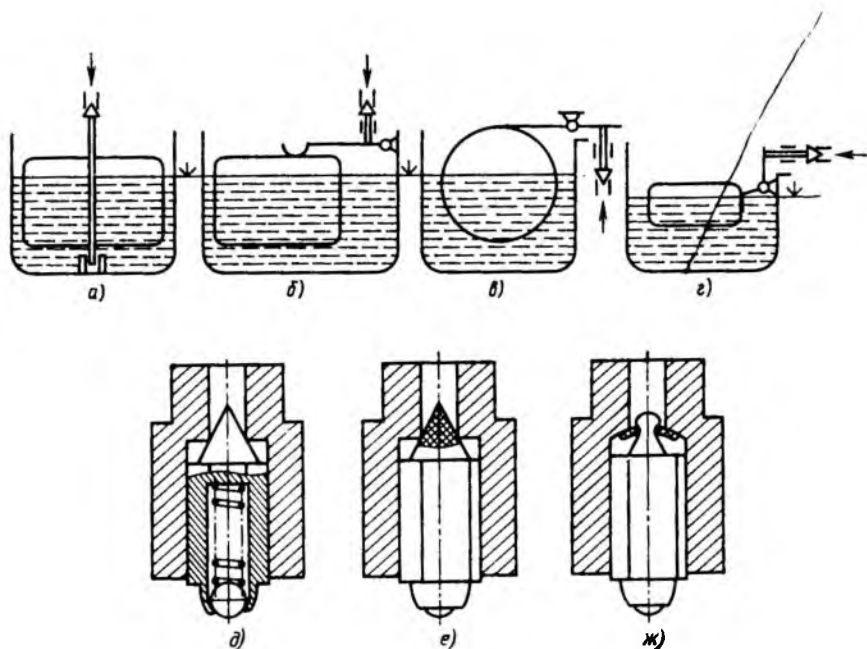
Поплавковая камера с различными запорными механизмами и конструкции запорной иглы
